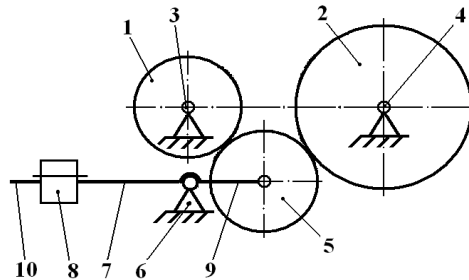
Схема фрикційної передачі з нерухомими опорами валів
